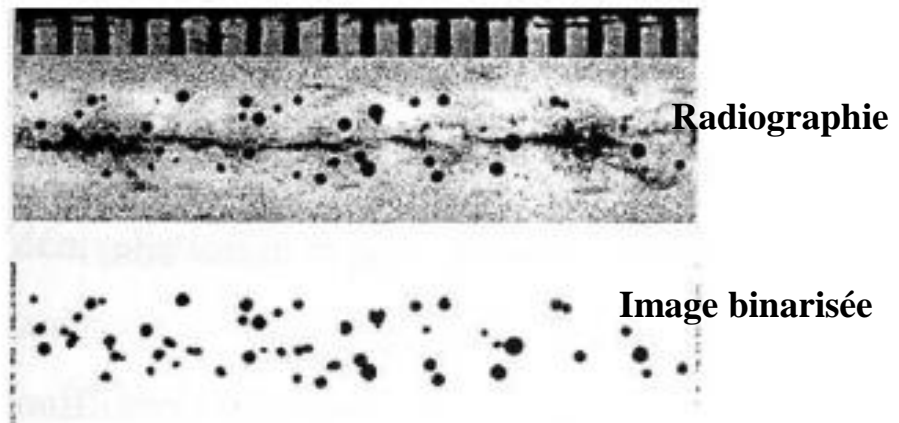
Porosité lors du soudage par laser CO<sub>2</sub> de tôles d'Al-Mg [31].
